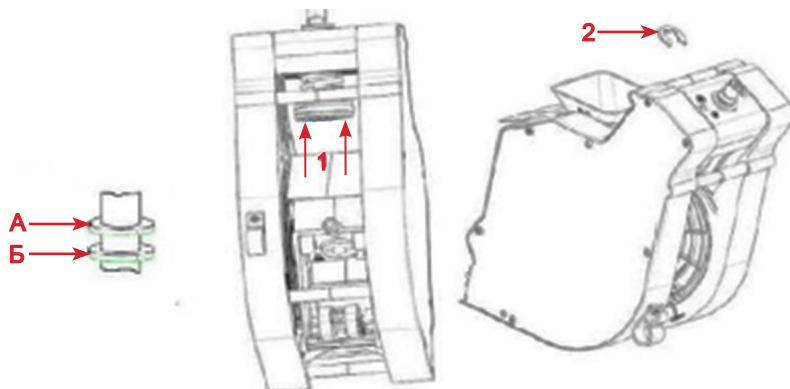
а - Регулировка объёма камеры группы эспрессо
